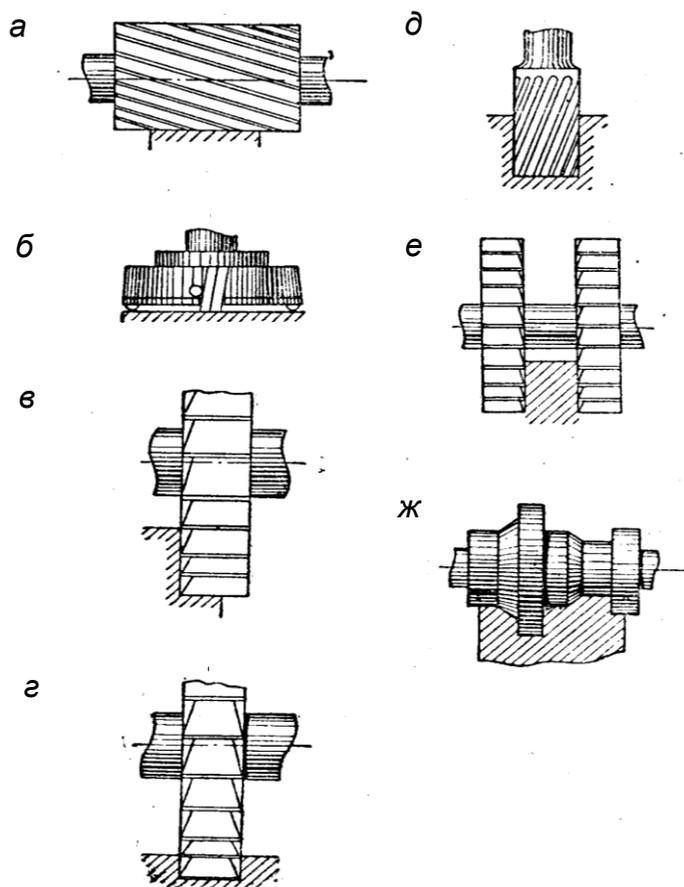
Различные виды обработки на фрезерных станках: а – обработка плоскости цилиндрической фрезой; б – обработка плоскости торцевой фрезой; в – обработка вертикальной плоскости дисковой трехсторонней фрезой; г – обработка паза концевой фрезой; е – обработка плоскости двумя
